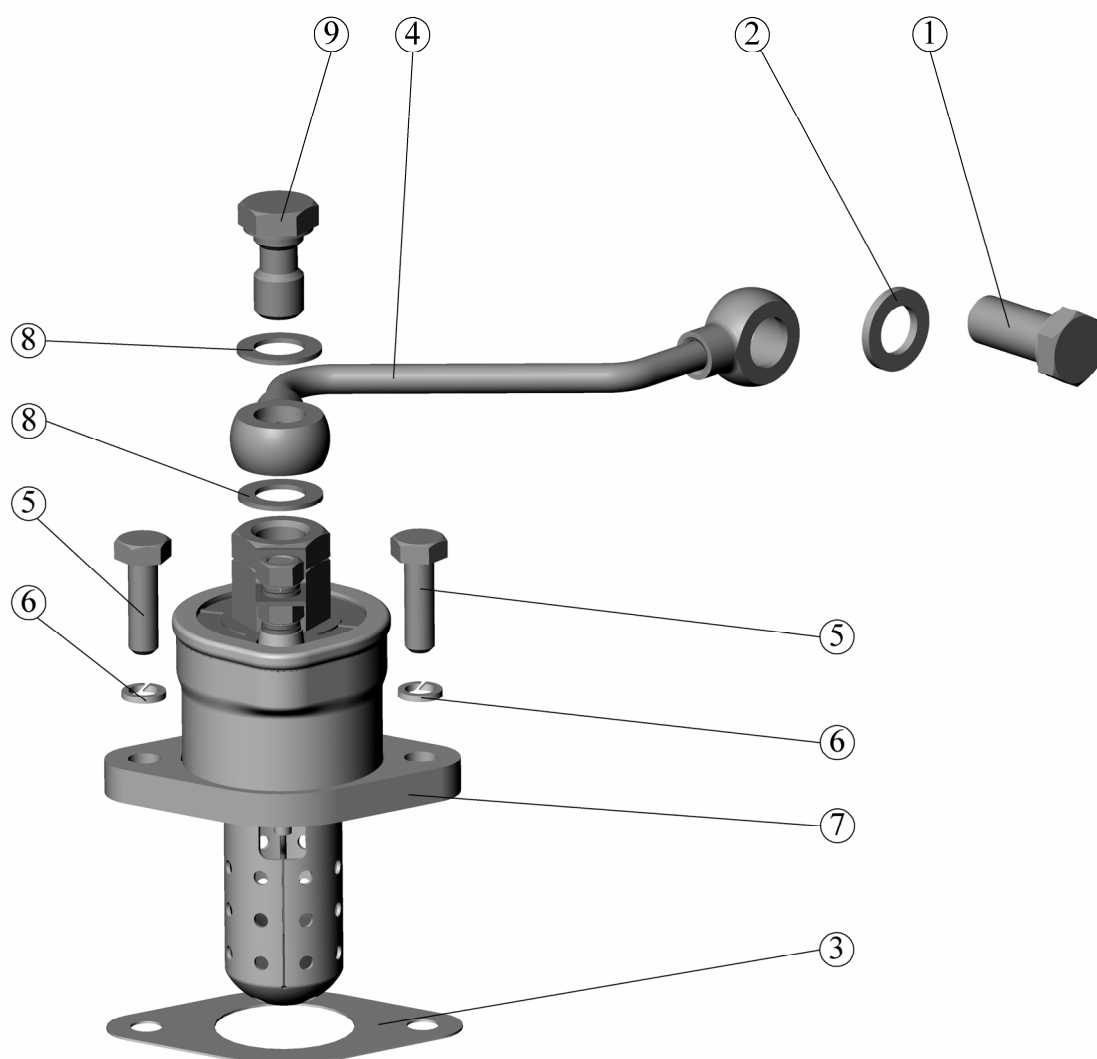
Установка электрофакельного подогревателя (для двигателей Д-242)
